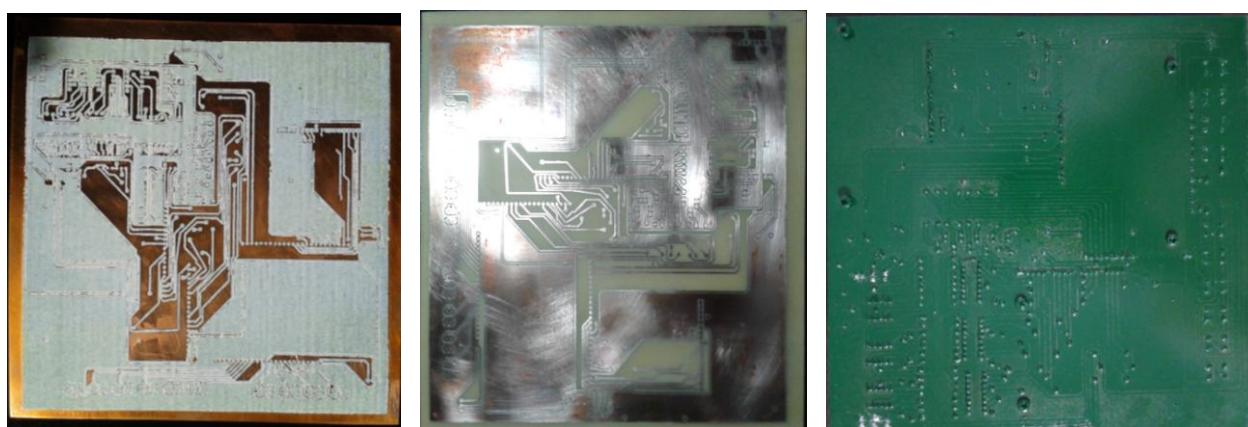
Processo de implementação da placa didática. Etapas de corrosão, perfuração e soldagem de componentes.
